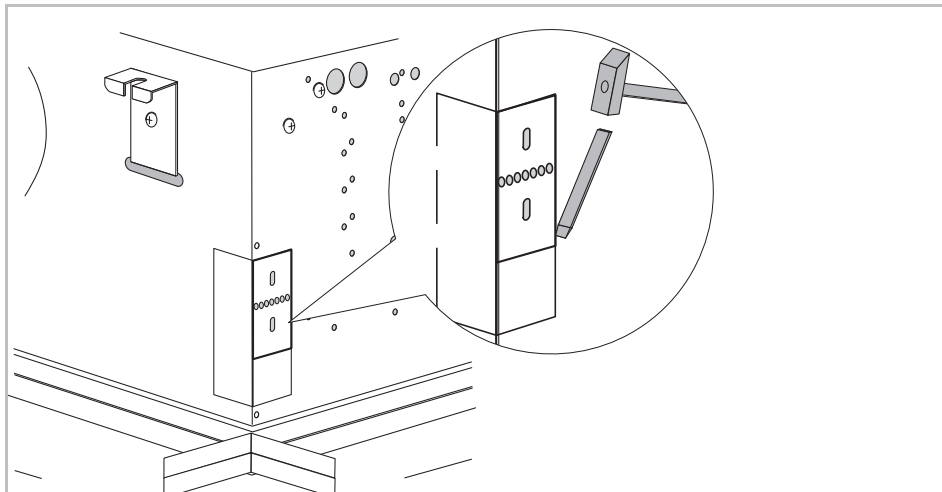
Přívod primárního vzduchu u typů jednotek Double a Big Single
